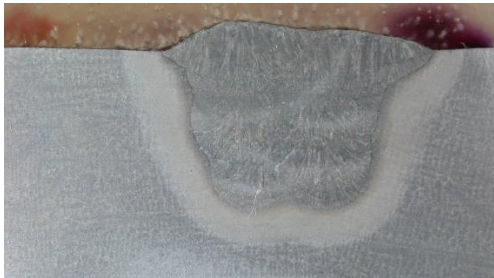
Makro výbrus, elektroda ϕ 5 mm
